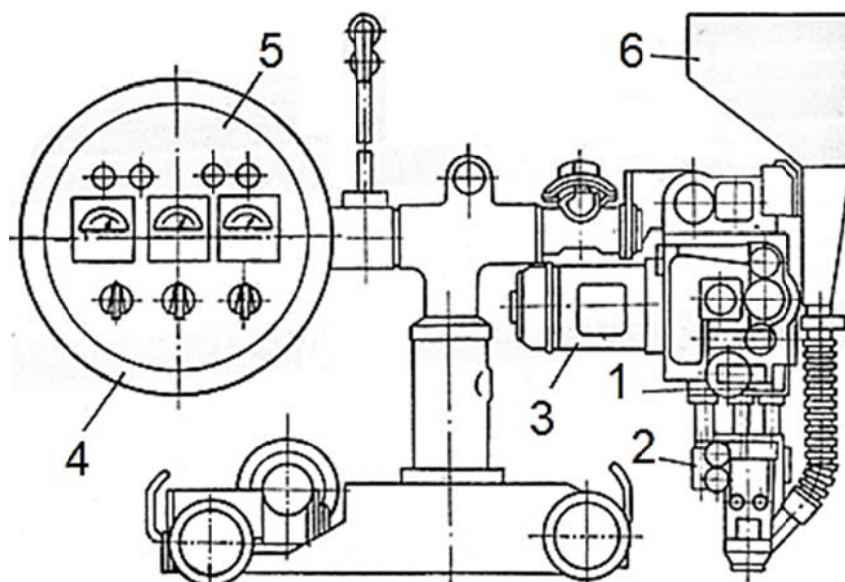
Общая схема сварочного трактора АДС-1000-4:
